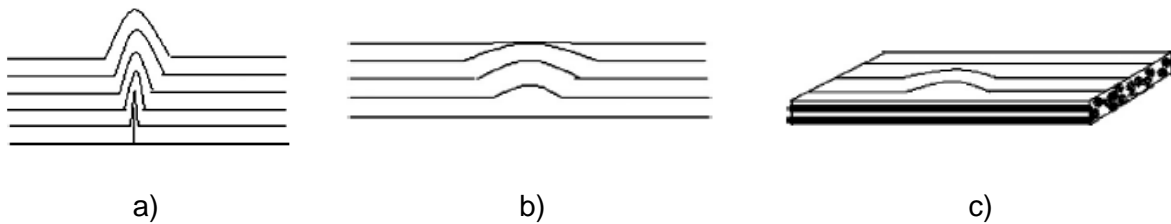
Schéma des 3 types de plissement, a) le plissement hors plan dit « wrinkle », b) le plissement hors plan dit « waviness » et c) le plissement dans le plan dit « in-plane waviness » [8]
